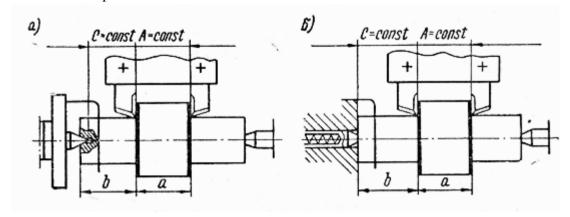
Обработка детали на жестком и плавающем передних центрах
